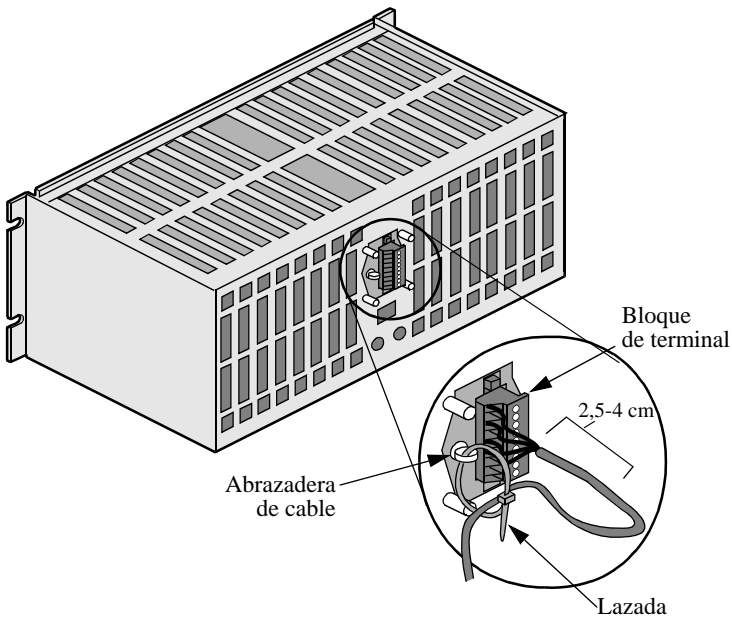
Soporte de bloque de terminal y cable del AccessWay
